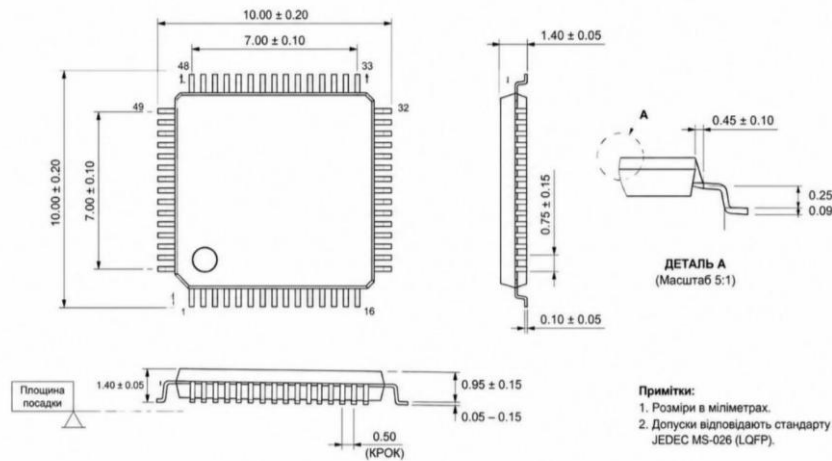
Зовнішній вигляд і розміри корпусу мікроконтролера STM32F446RET6
